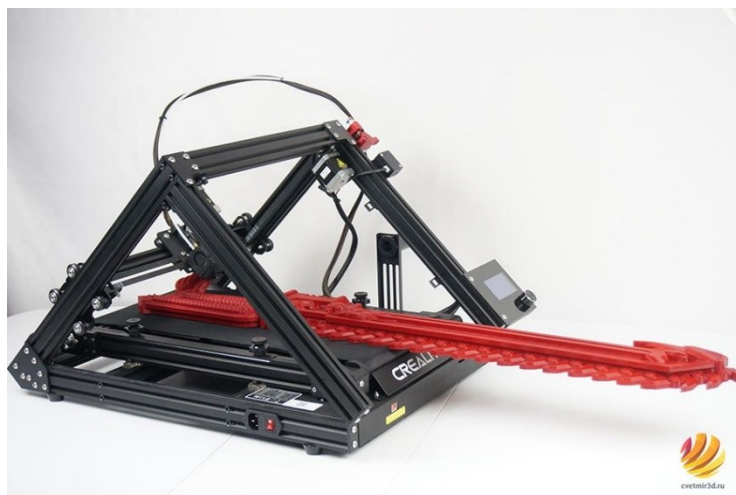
3D-принтер Creality 3DPrintMill
